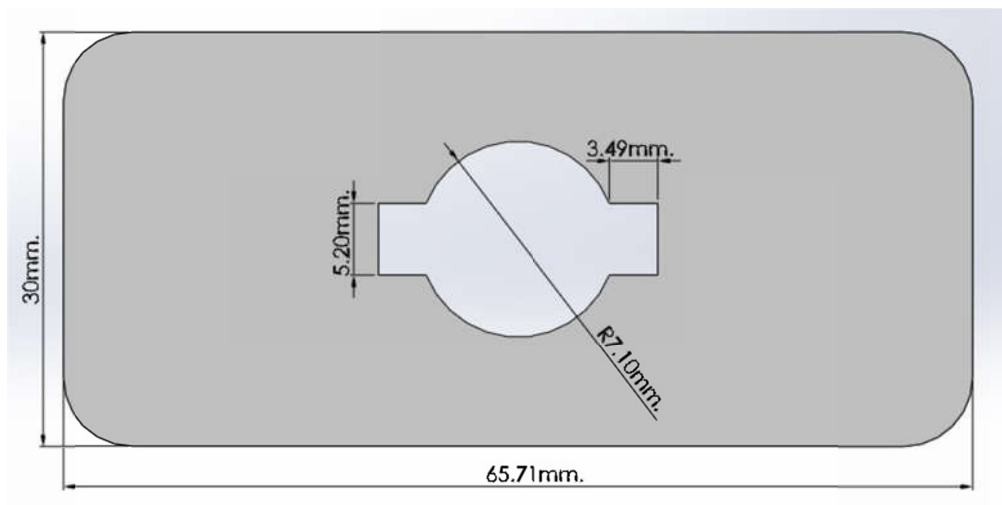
Pieza 5 del soporte para introducir las bobinas y la punta de prueba al magnetómetro.
